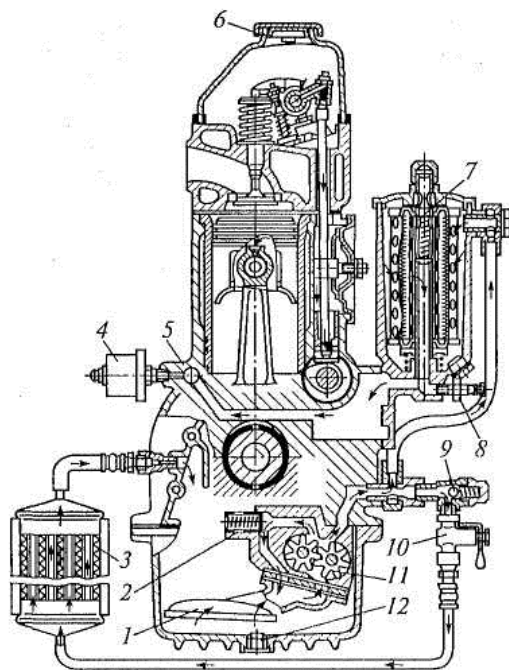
Смазочная система двигателей легковых автомобилей ГАЗ:
